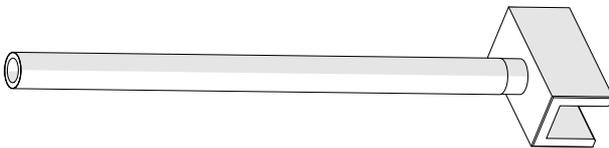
Richtwerkzeug 0812 Verdrillung (Bestell-Nr.: 08-W100-0594)
